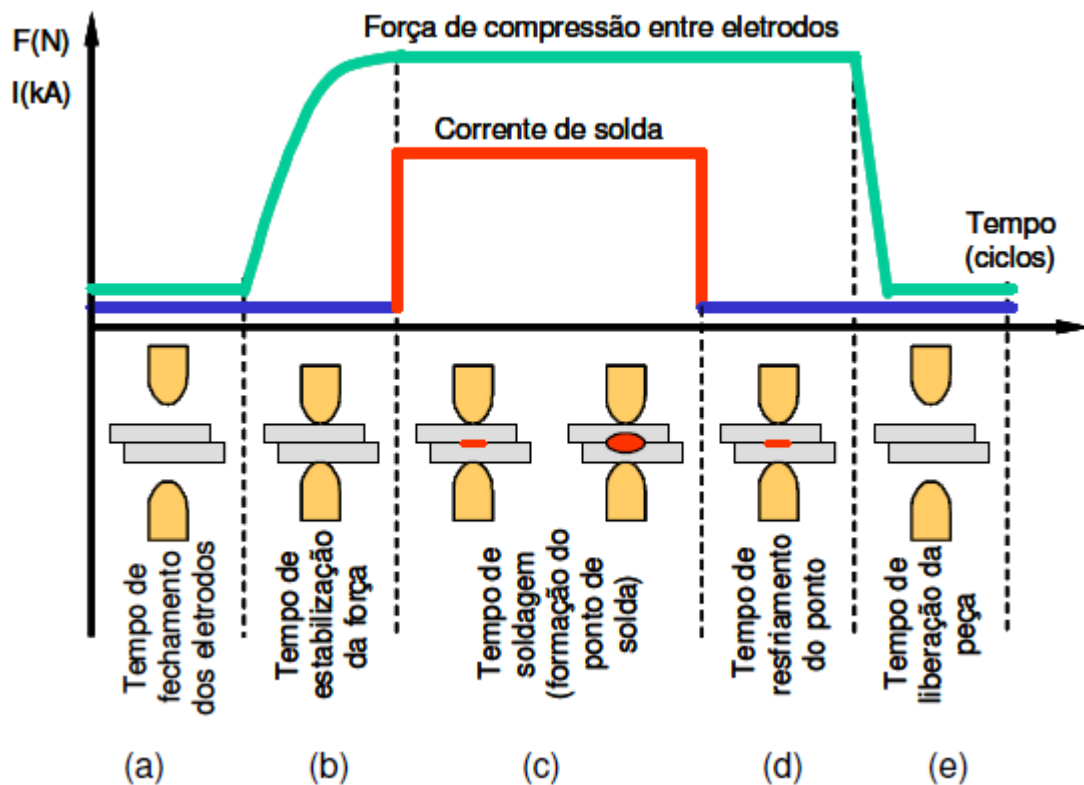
Etapas do ciclo de soldagem -Fonte: Welding, 2009.
